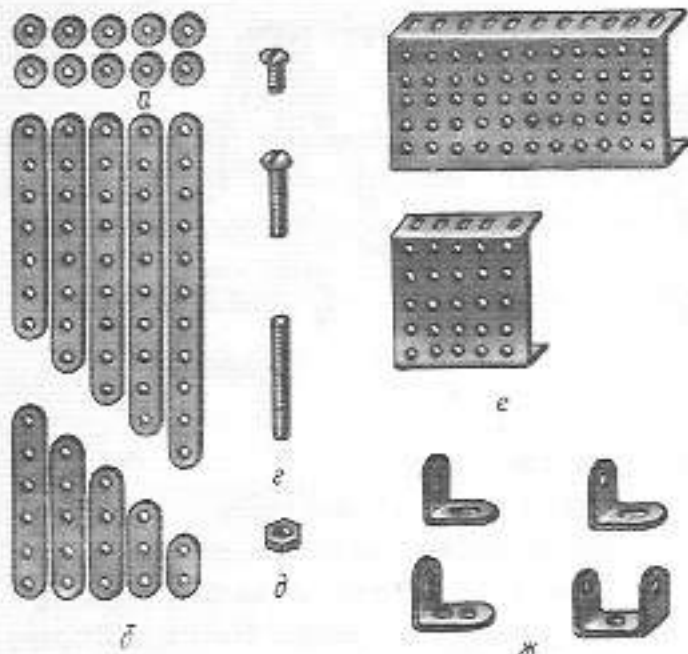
Детали металлического конструктора: а — шайбы; б — полосы; в — винты; г — шпилька; д — гайка, е — платы; ж — уголки.
